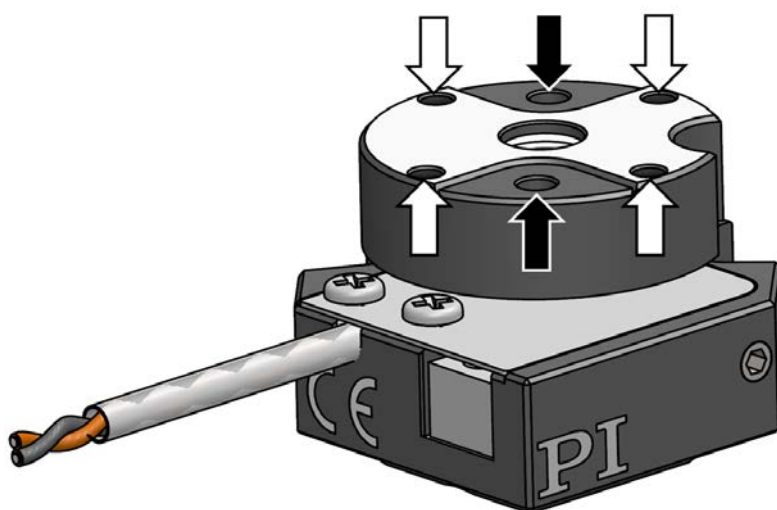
Schwarze Pfeile bezeichnen die Passbohrungen zum Ausrichten der Last, weiße Pfeile bezeichnen Gewindebohrungen zum Befestigen der Last
